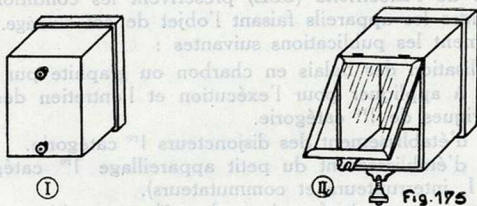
Deux exemples de réalisation de boîtiers d'appareils muraux.
